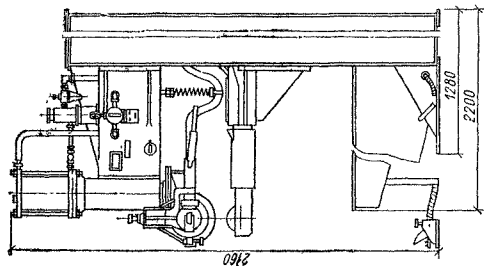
Машина МШП-100 для контактной сварки с продольным расположением роликов
